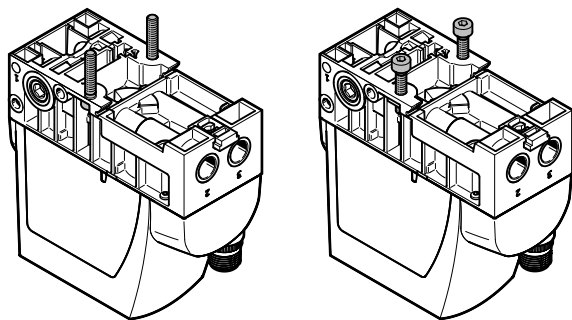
Befestigung über Ventilunterseite mit Schrauben M4/Schrauben M4 und Vierkantmuttern
